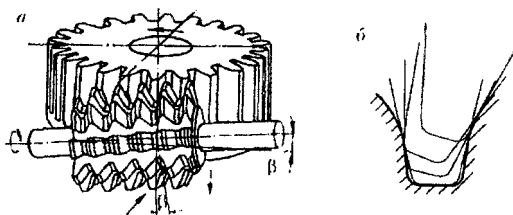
Схема зубофрезерования прямых зубьев колеса червячной фрезой
